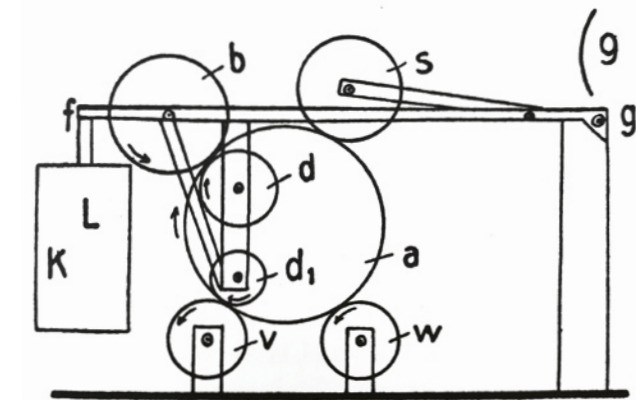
Technische Zeichnung (Figur 9), in: Paul Scheerbart, „Das Perpetuum mobile – Die Geschichte einer Erfindung“, Leipzig 1910
